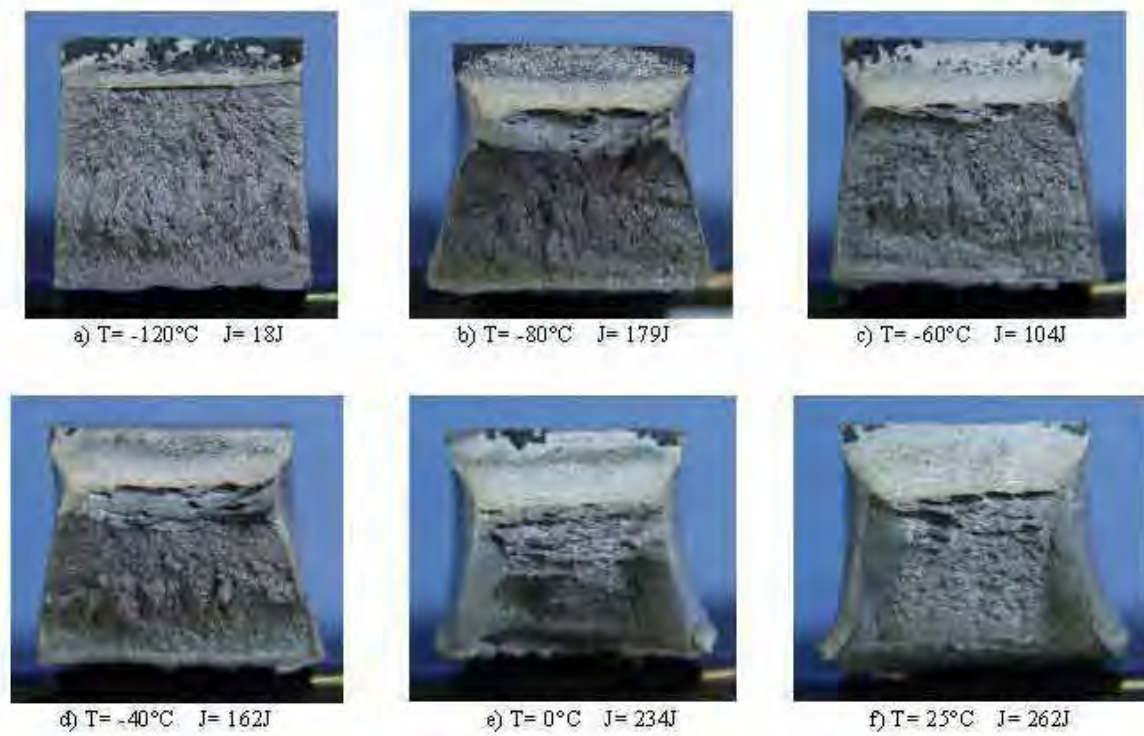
Fractografia da superfície de fratura do aço API- R23 °C/s, corpo-de-prova entalhado.
